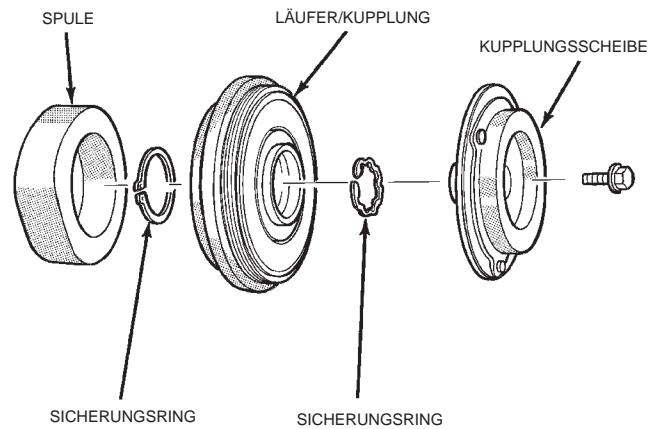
Kompressorkupplung - Fahrzeuge mit Ottomotor
